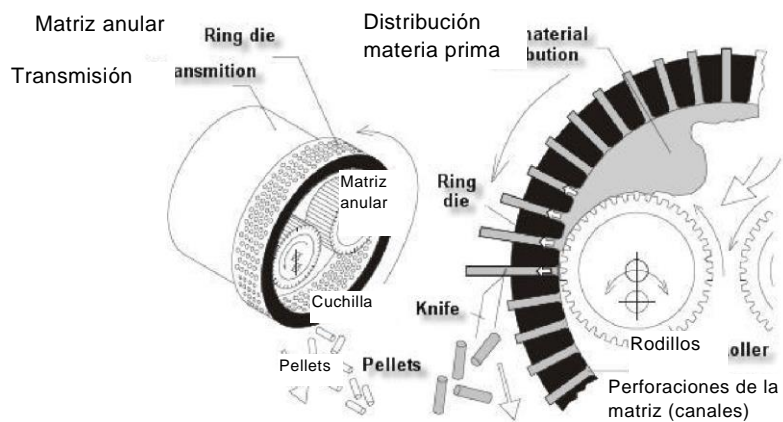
Vista esquemática de un molino de pellets de matriz cilíndrica. Fuente: Safety Engineering
